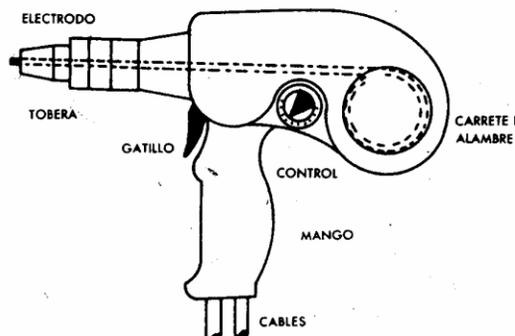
Pequeña pistola portátil para M.I.G.
